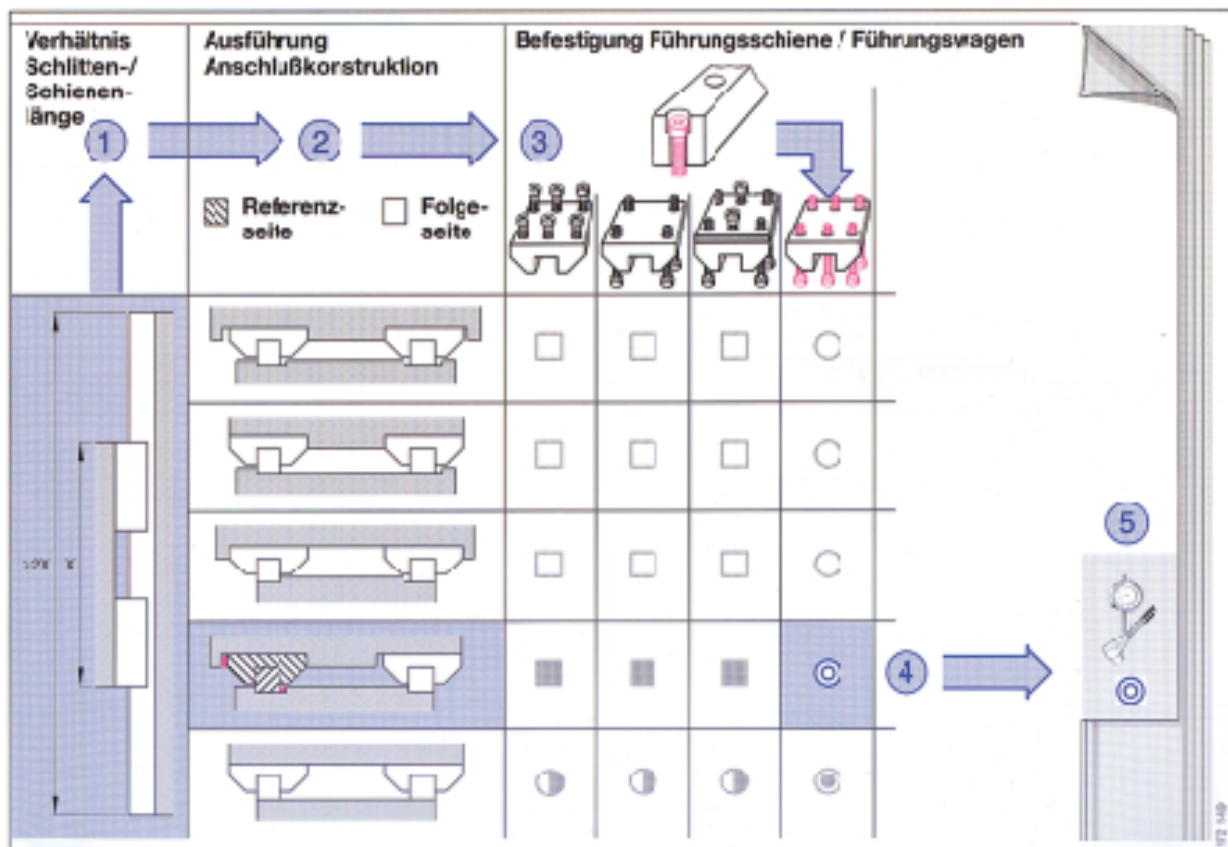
Linearführungen [3] – Montagevariante bestimmen
